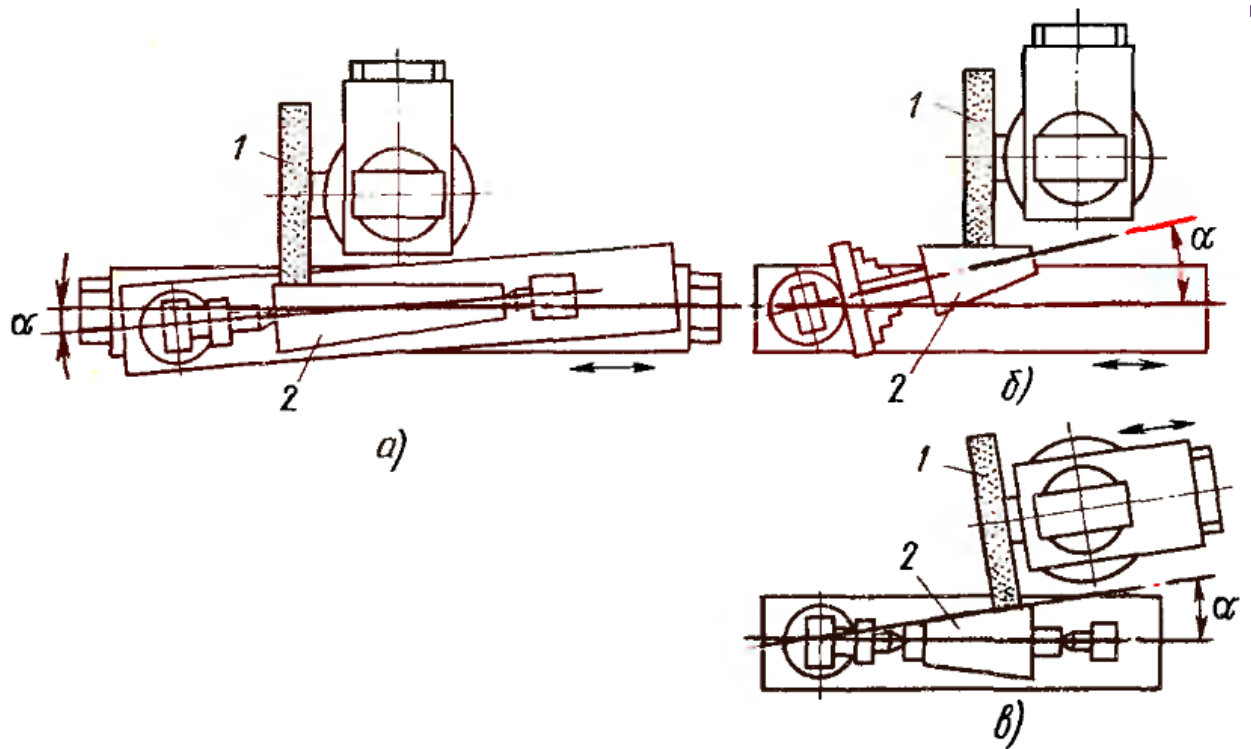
Шлифование конических поверхностей путем установочного поворота на половину угла при вершине конуса: а — стола, б — передней бабки, в — шлифовальной бабки; 1 — шлифовальный круг, 2 — заготовка
